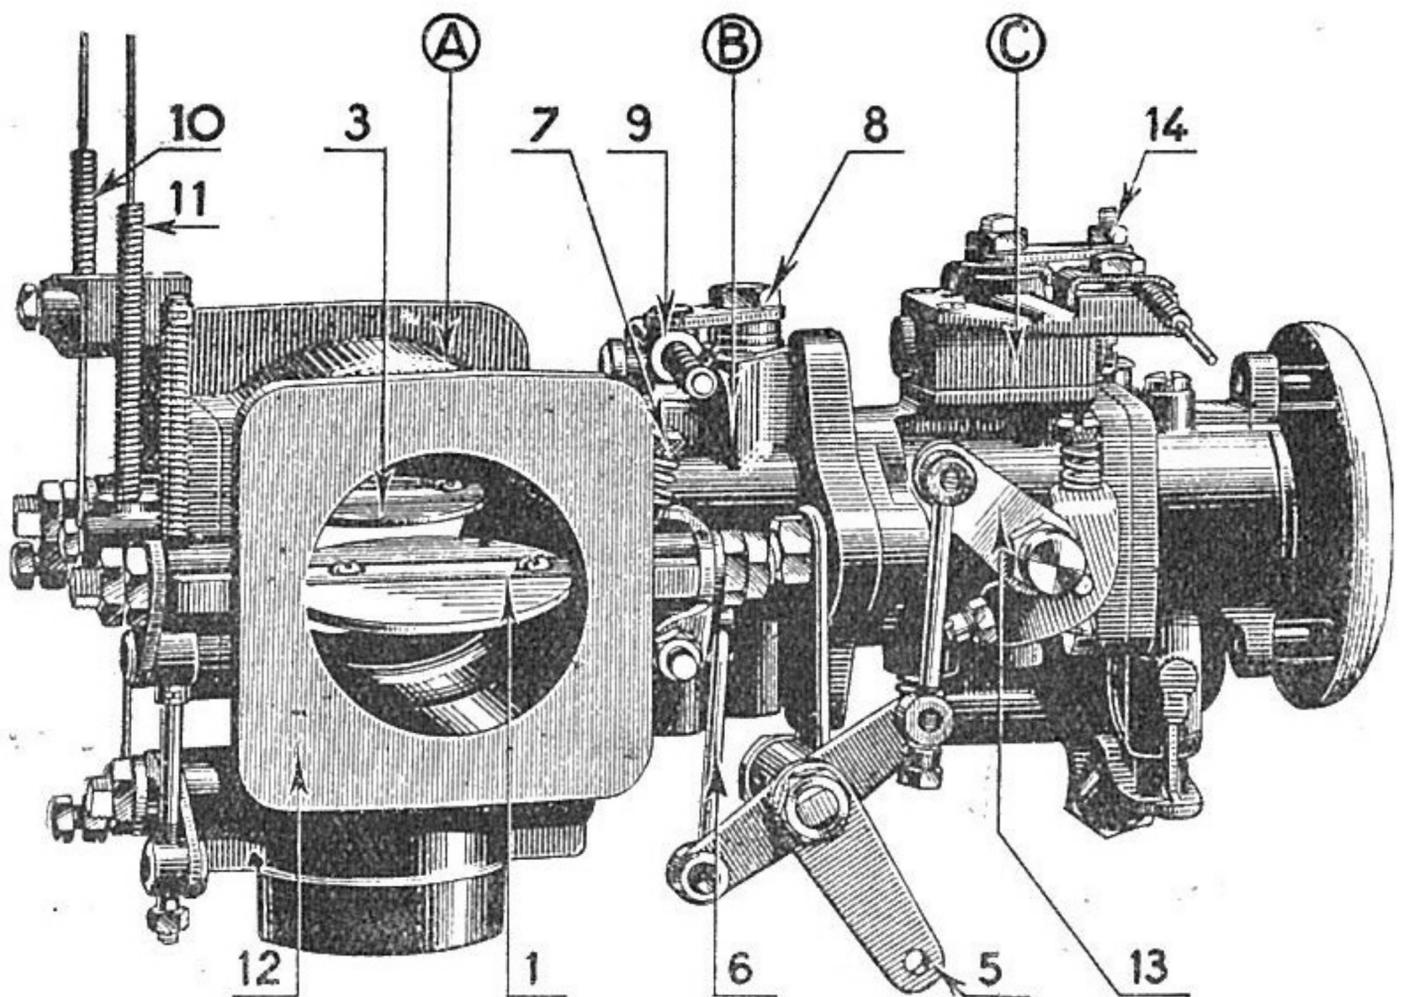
Le Carburateur-Mélangeur Solex, vu côté moteur, orienté horizontalement.
